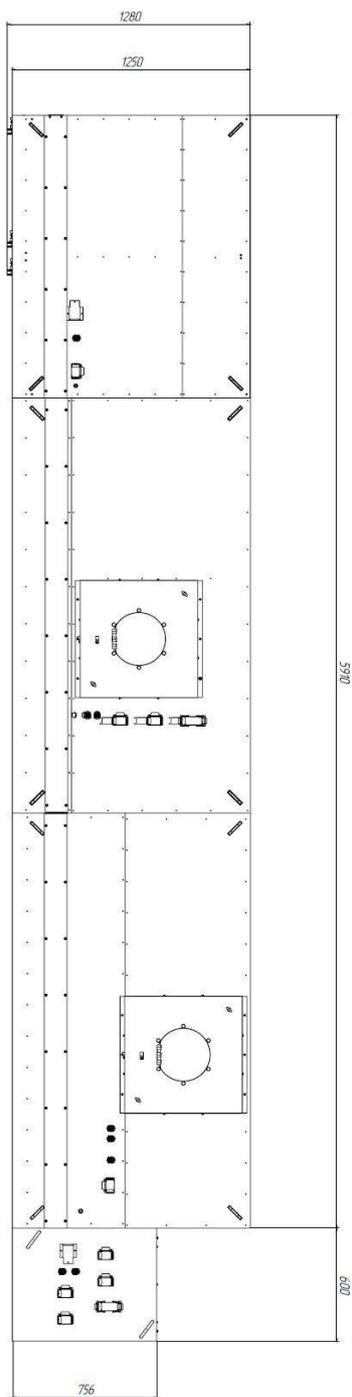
АТ27-М80...1М6-6/6-XXXXXX-С-43. Вид сверху
